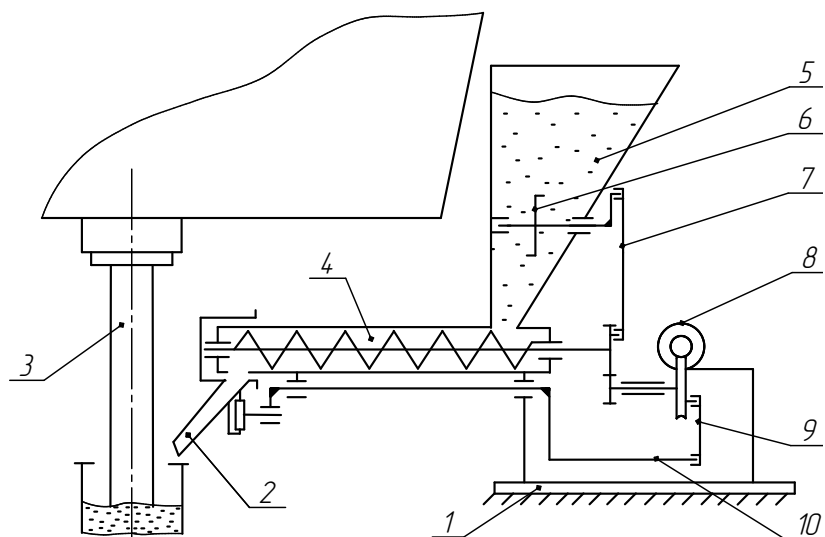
Конструктивная схема предлагаемой установки механизированной подачи ШОС в кристаллизатор блюмомой МНЛЗ
